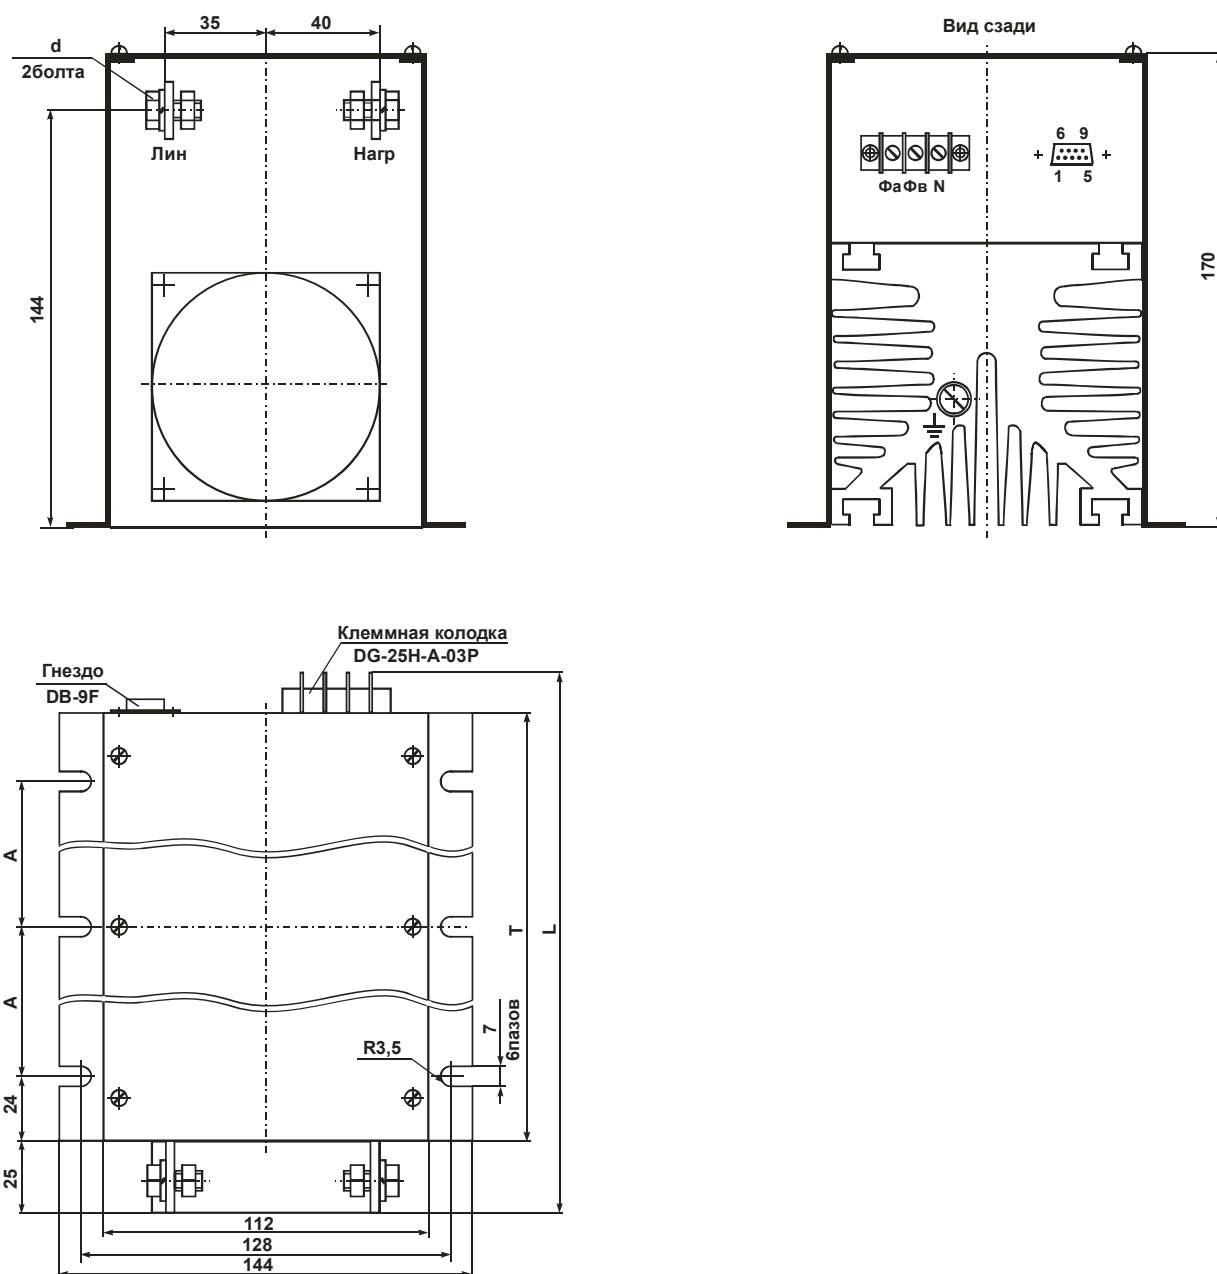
Габаритные и присоединительные размеры TRM1
